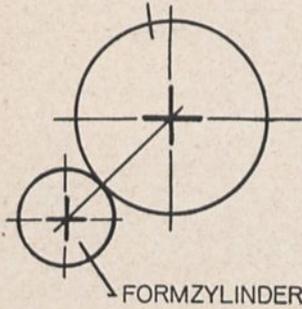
Schema der gebräuchlichsten Druckwerksanordnung bei modernen Rakeltiefdruckmaschinen; der Formzylinder befindet sich schräg unterhalb des Druckzylinders
